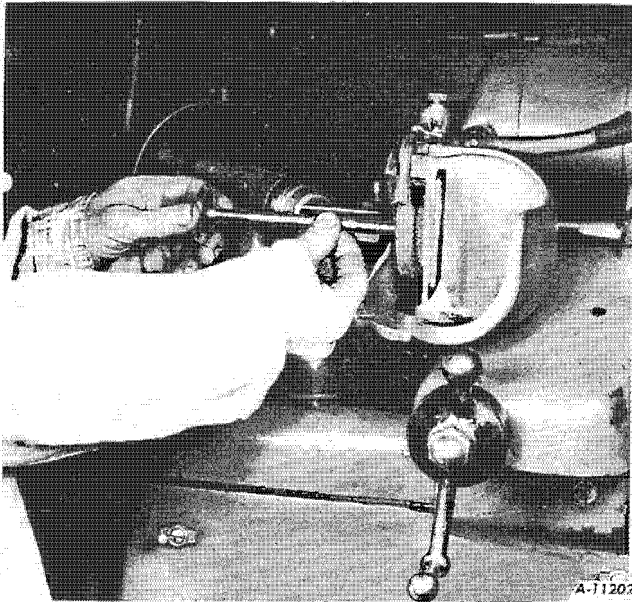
C - Meulage de l'extrémité de la queue de soupape.
